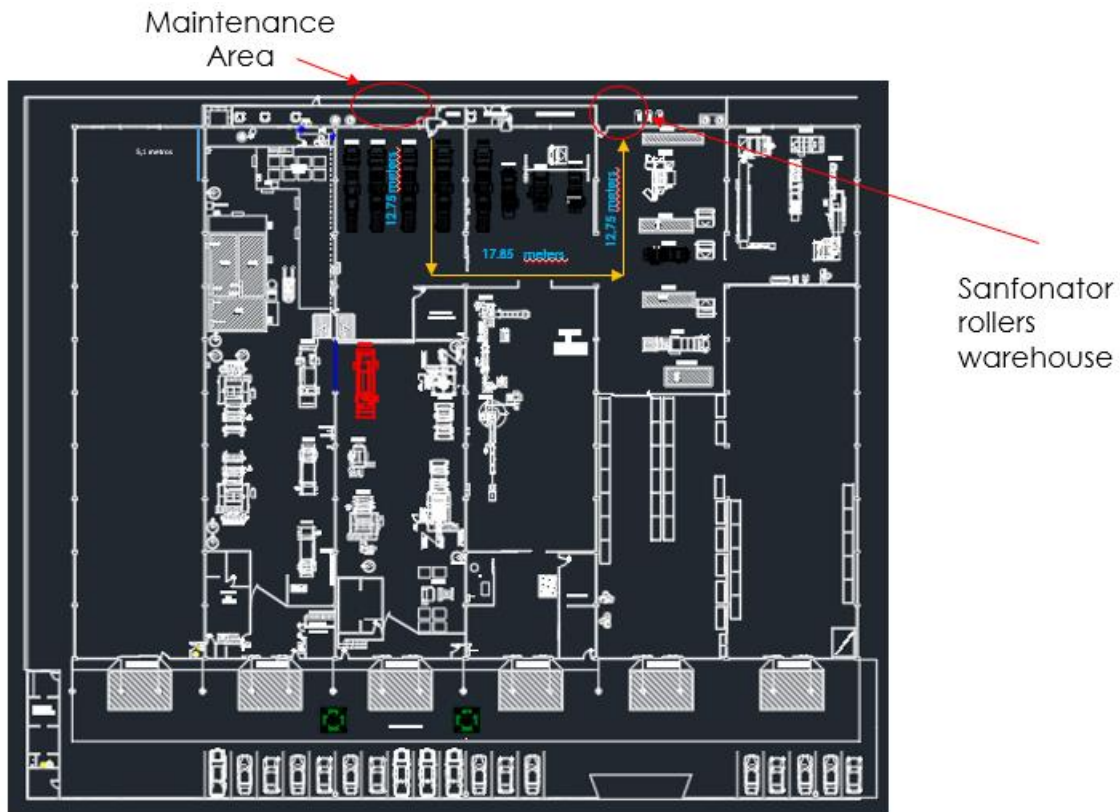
Layout de la empresa (Facilitado por la empresa)
